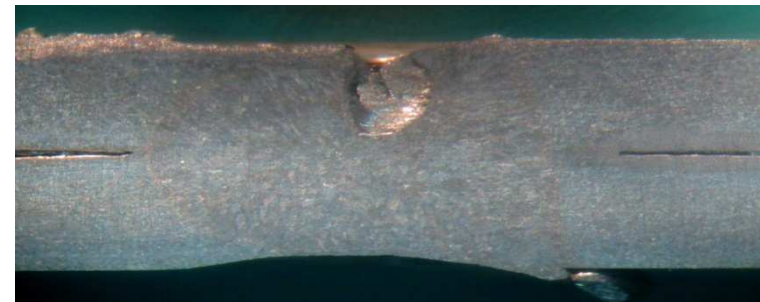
11. Macrografía del punto de soldadura en la probeta de 2 mm a 10x.
